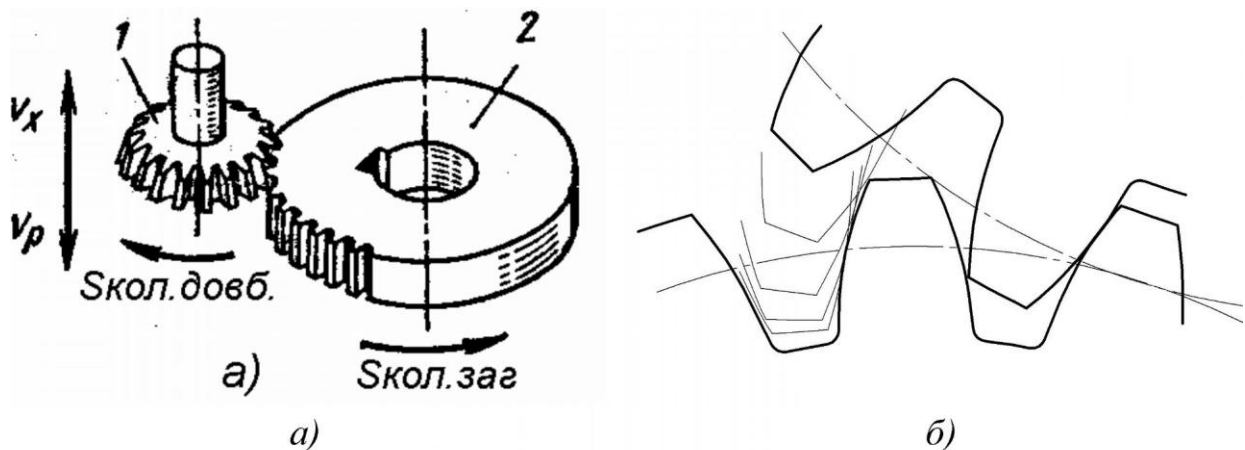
Схема формоутворення зубів циліндричного колеса
